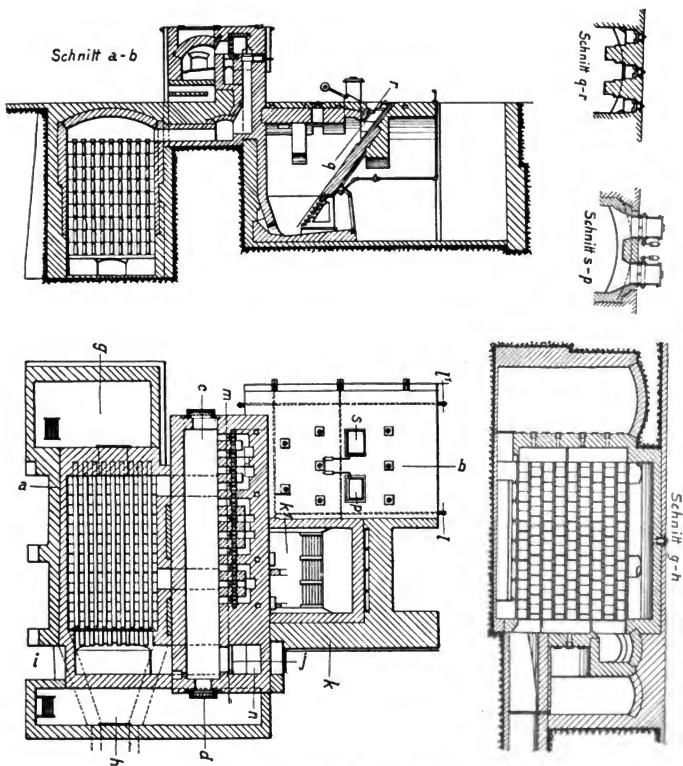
b. Rekuperator-Röhrenschweißofen.
